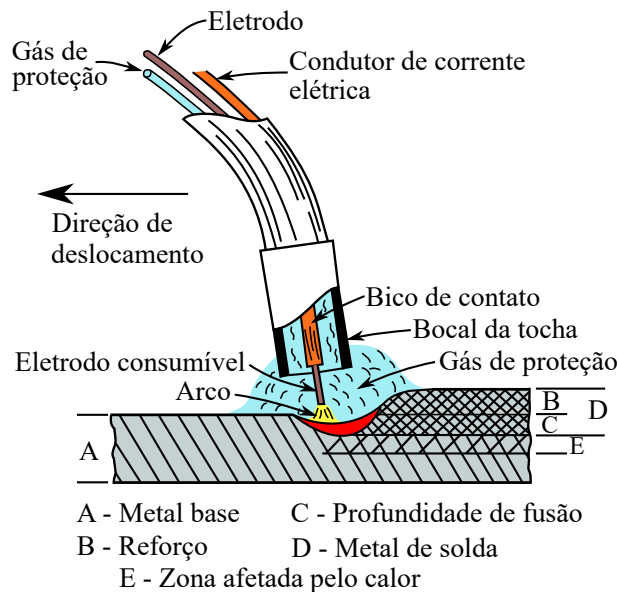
Visão geral do processo de soldagem MIG/MAG [adaptado de AWS, 2004].
